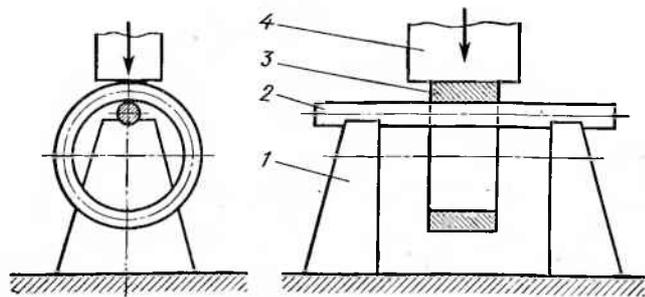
Схема раскатки на оправке: 1 — стойка, 2 — оправка, 3 — заготовка, 4 — верхний боек
